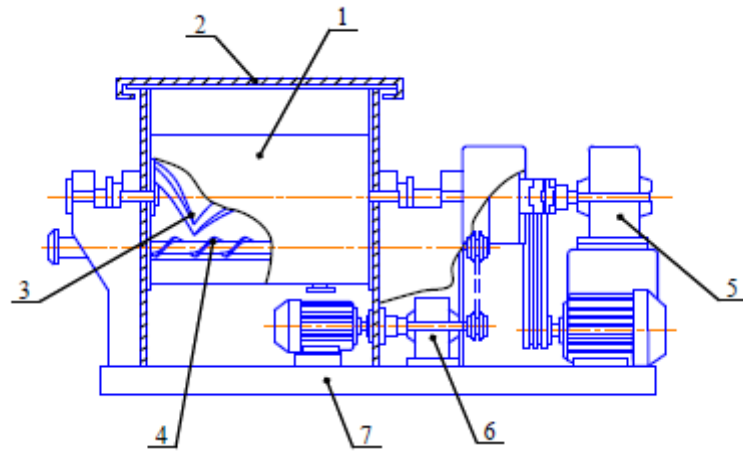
Двох лопатевий змішувач із реверсивним шнеком типу СРШ: 1 – камера змішування; 2 – кришка; 3 – валки; 4 – реверсивний шнек; 5 – привід валків; 6 – привід шнека; 7 – станина
